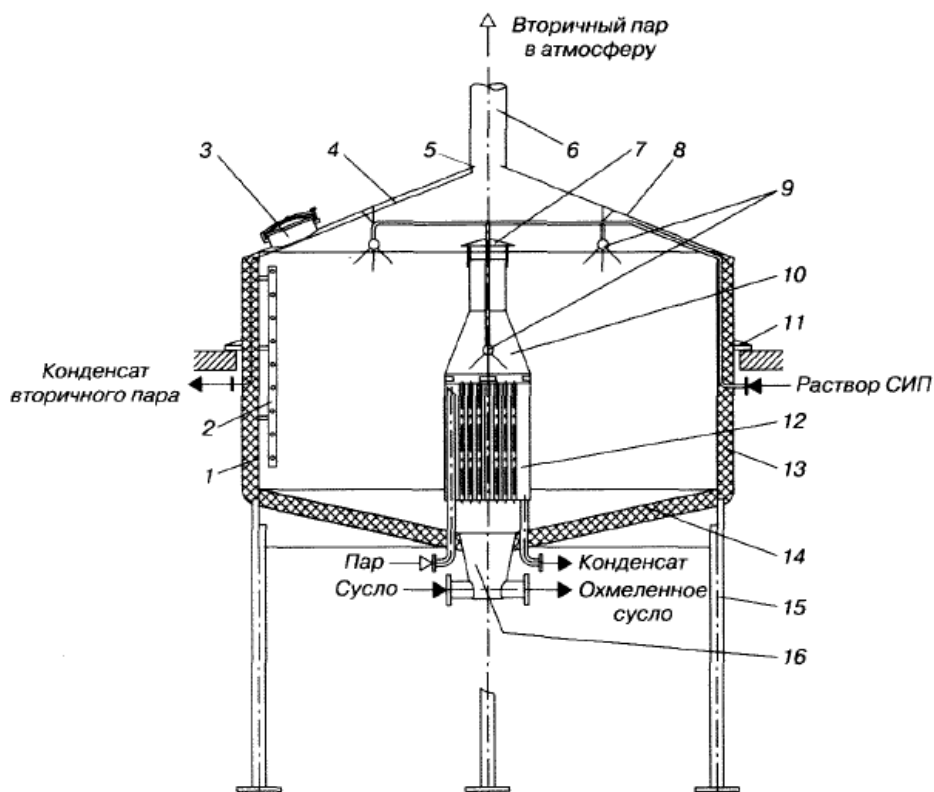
Сушварочный аппарат с внутренним нагревателем.
